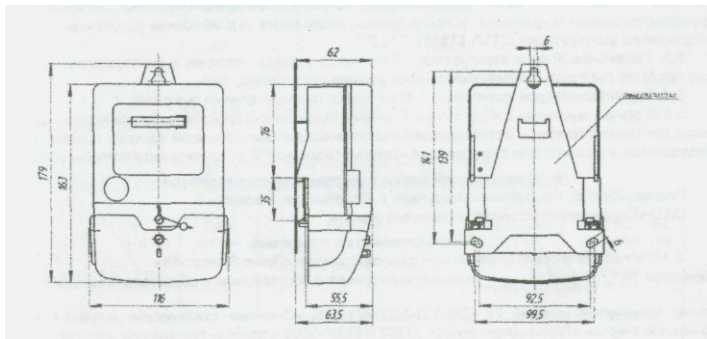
Общий вид счетчика в корпусе типа P1 с переходной планкой на стандартное крепление
